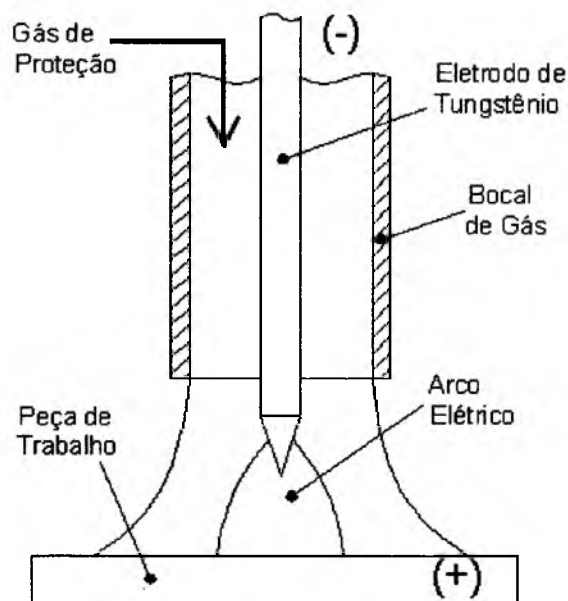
Representação Esquemática do Processo de Soldagem TIG
